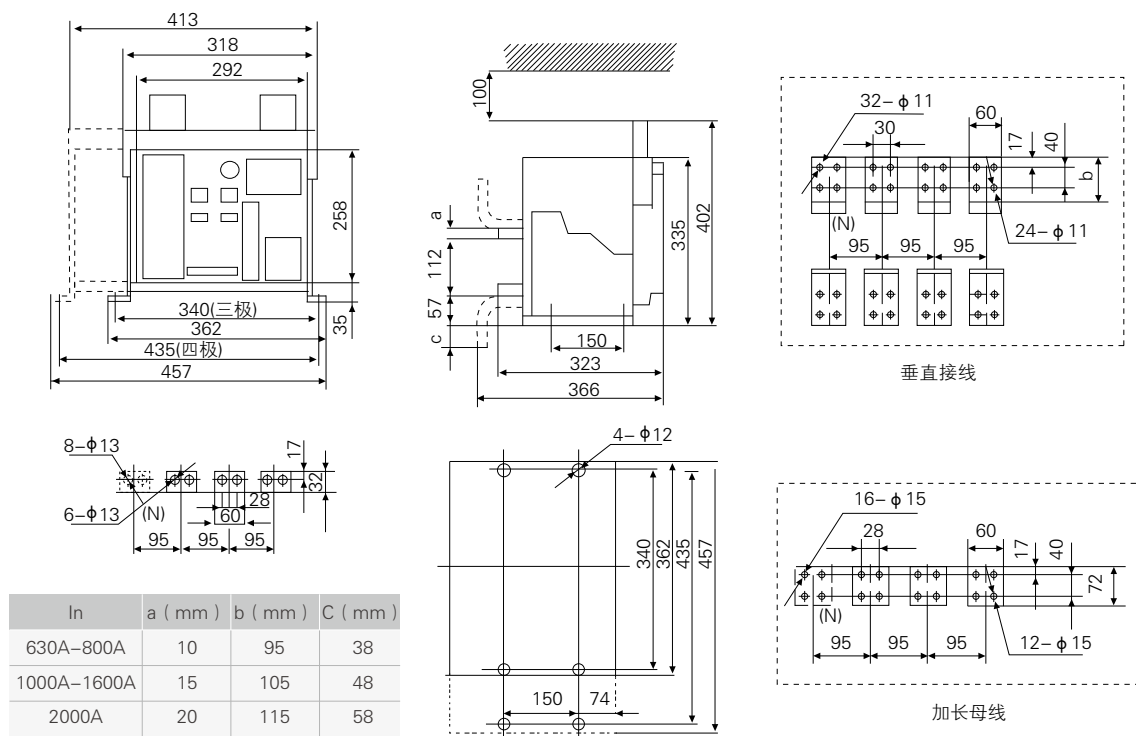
固定式断路器安装尺寸及外形尺寸 (BW1-2000)
